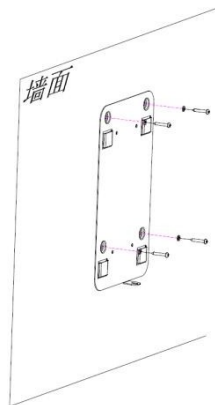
Схема кріплення настінних кронштейнів
